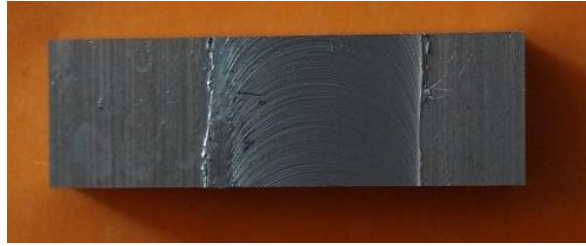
Espécimen vista superior de la soldadura.
